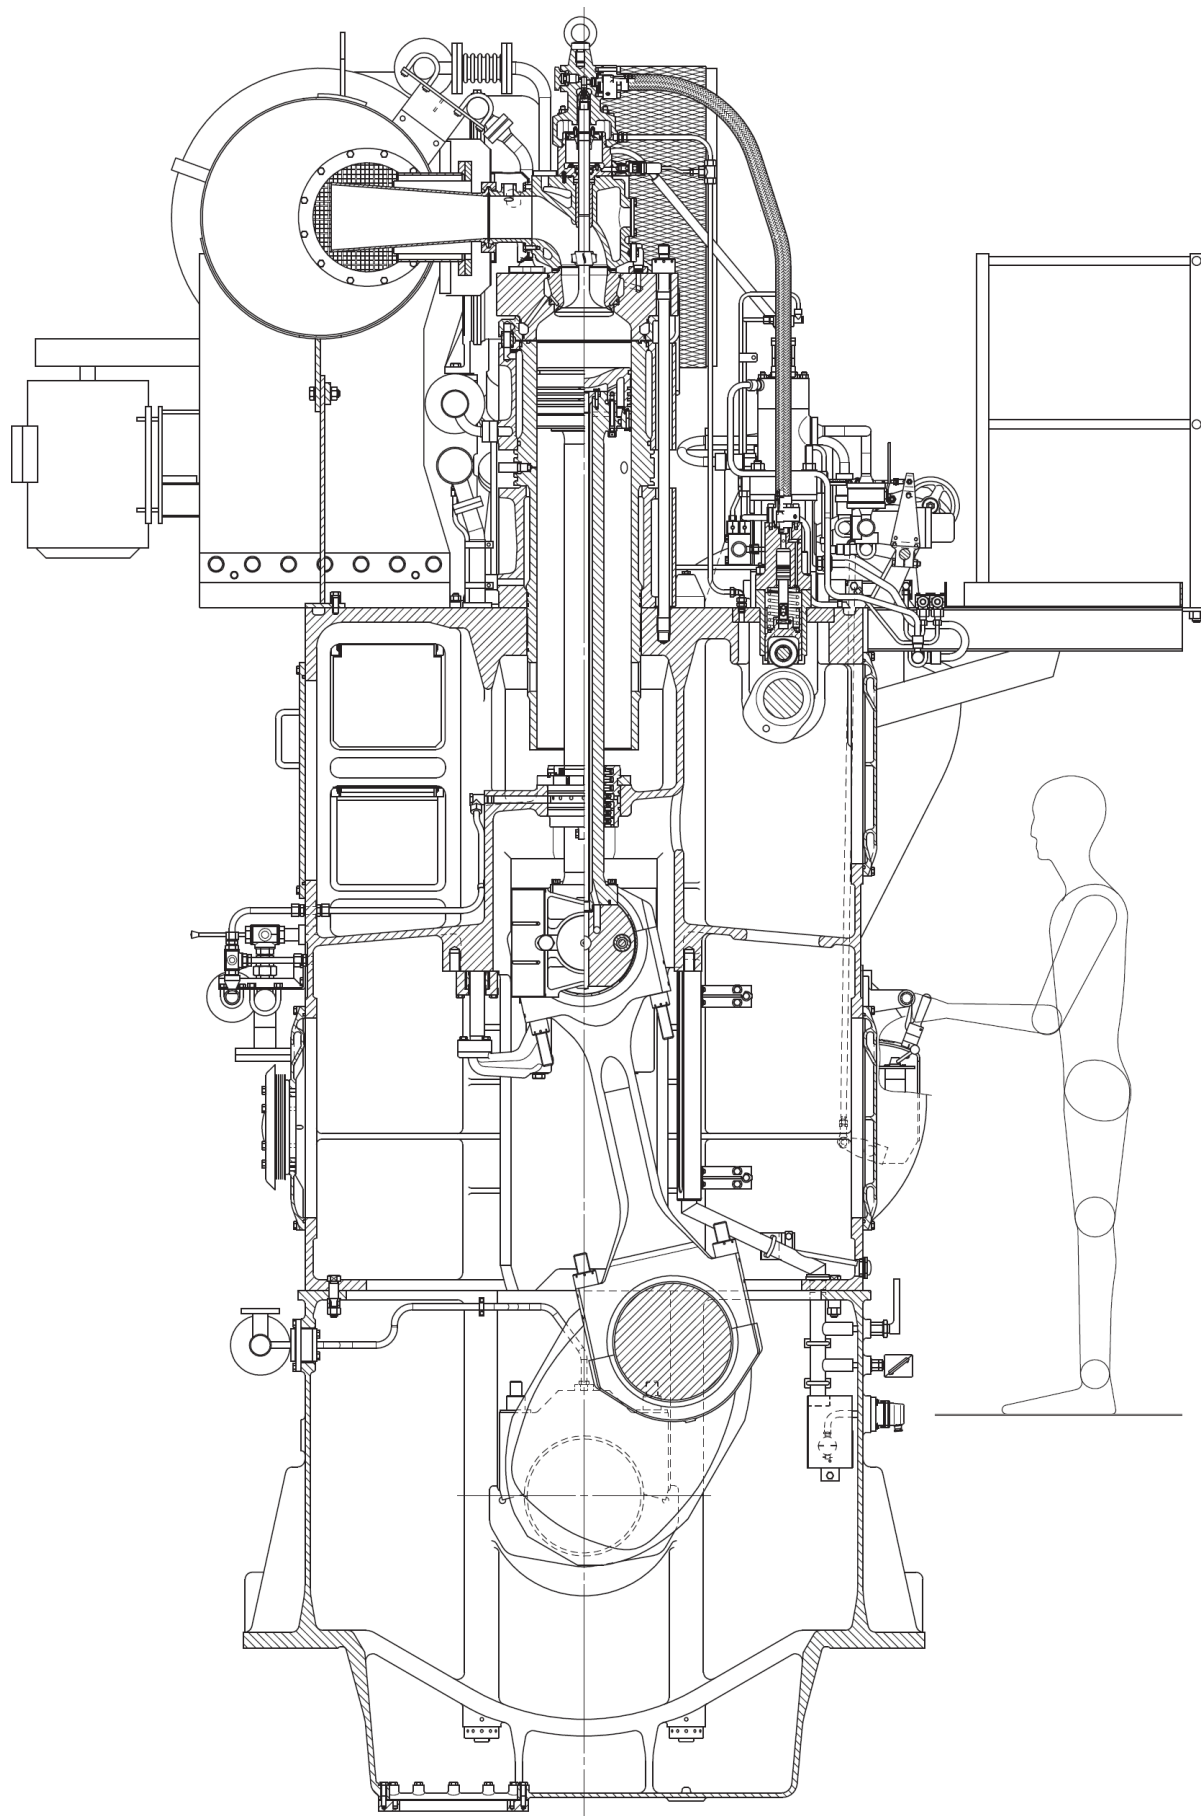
Креслення конструкції двигуна 6ДКРН 26/98
